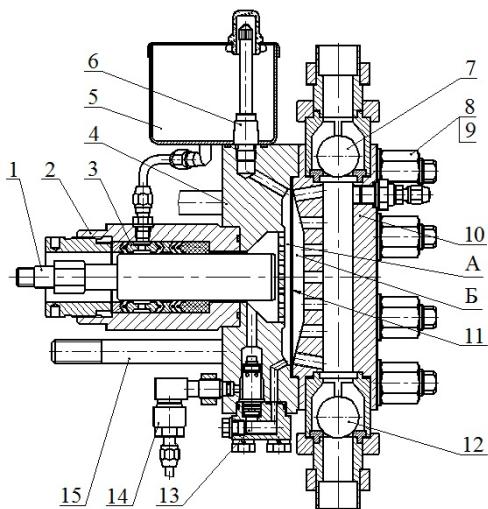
Мембранный головка с дифференциальным подпиточным клапаном: 1 – плунжер; 2 – цилиндр; 3 – узел уплотнения плунжера; 4 – половина корпуса левая; 5 – бак; 6 – воздухоотделитель; 7 – нагнетательный клапан; 8 – гайка; 9 – шпилька; 10 – половина корпуса правая; 11 – мембрана; 12 – всасывающий клапан; 13 – клапан подпиточный; 14 – клапан обратный; 15 – шпилька
